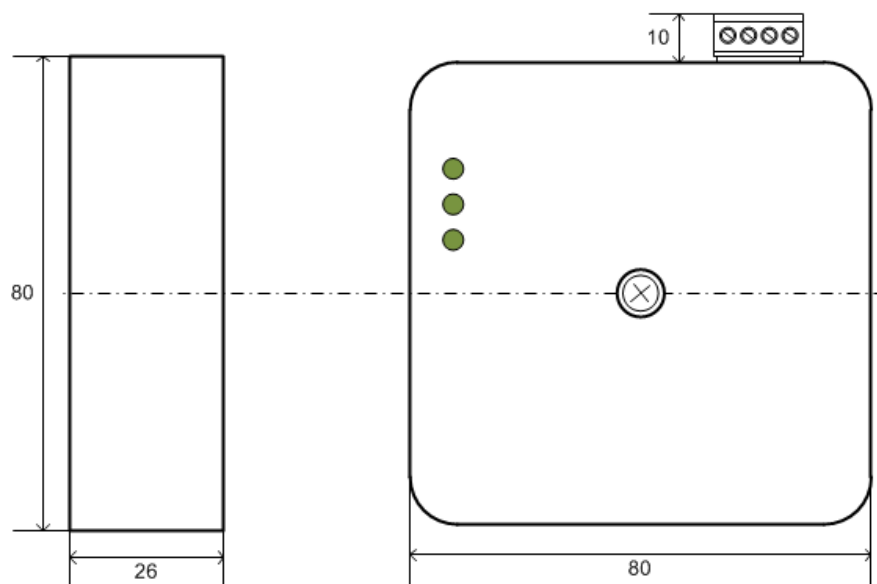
Габаритные размеры корпуса, без адаптера ДИН-рейки.
